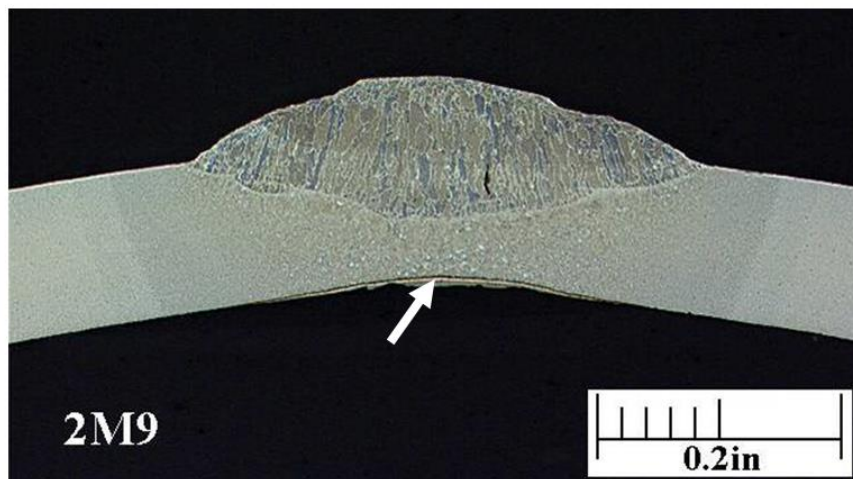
Макроструктура зварного з'єднання при наплавленні валика на поверхню труби [216]
